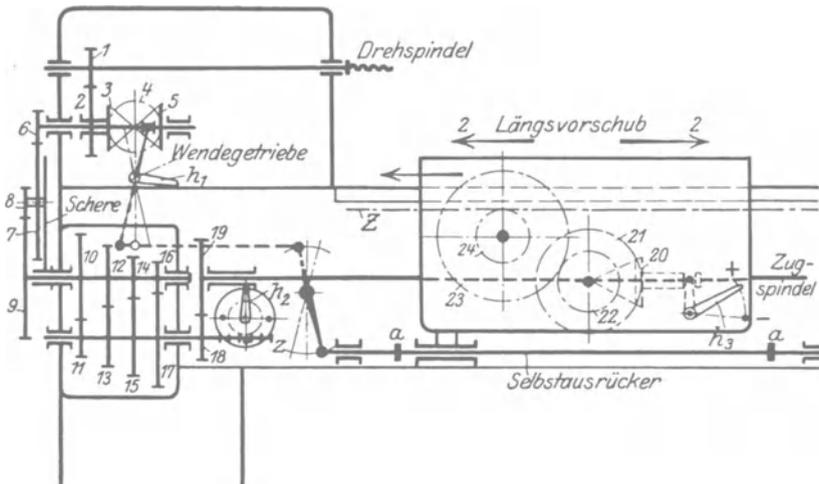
Längszug mit Zahnstange für eine Bolzendrehbank.
